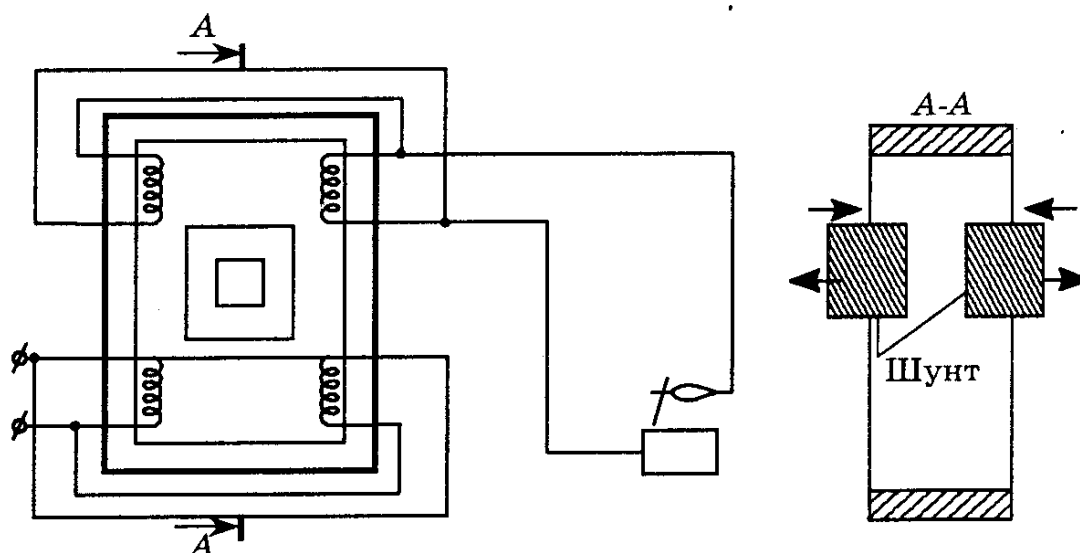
Электрическая схема сварочного трансформатора типа СТШ 500-80
